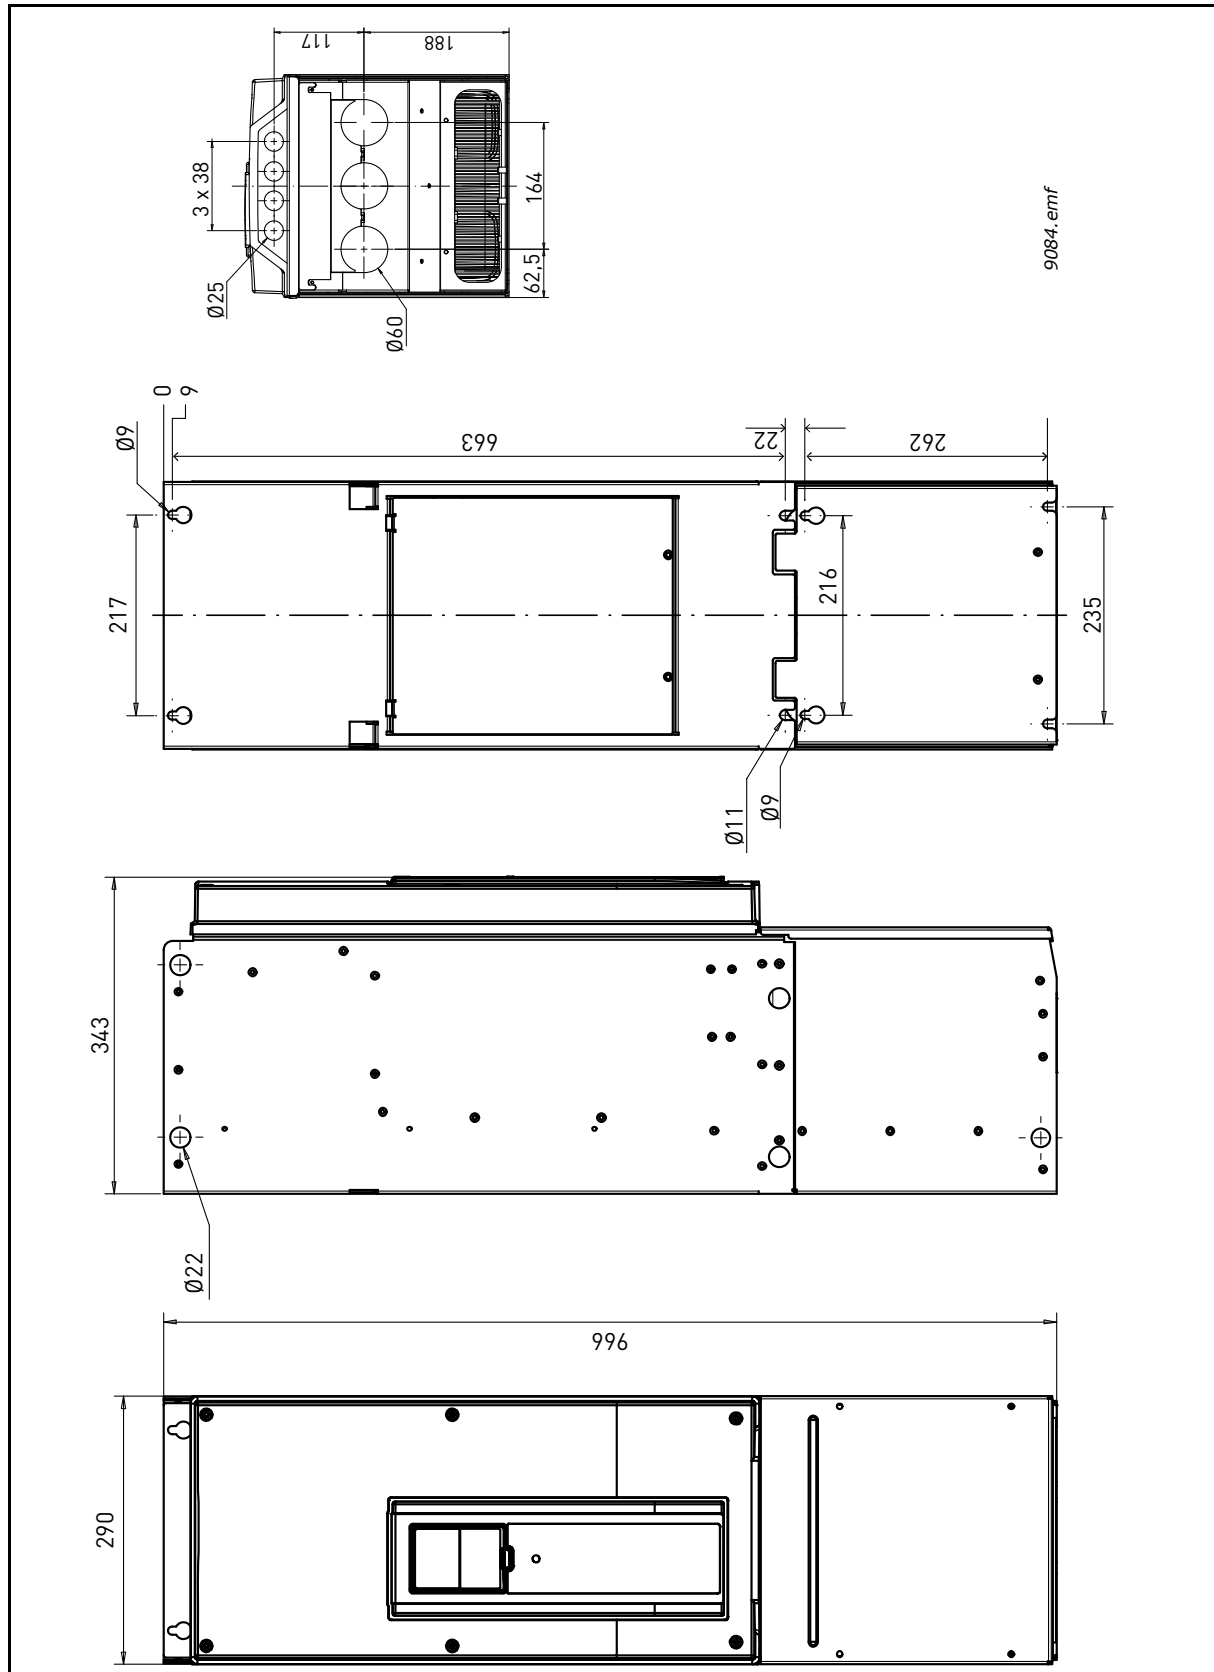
Dimensioner for Vacon-frekvensomformer, MR5, vægmontering
